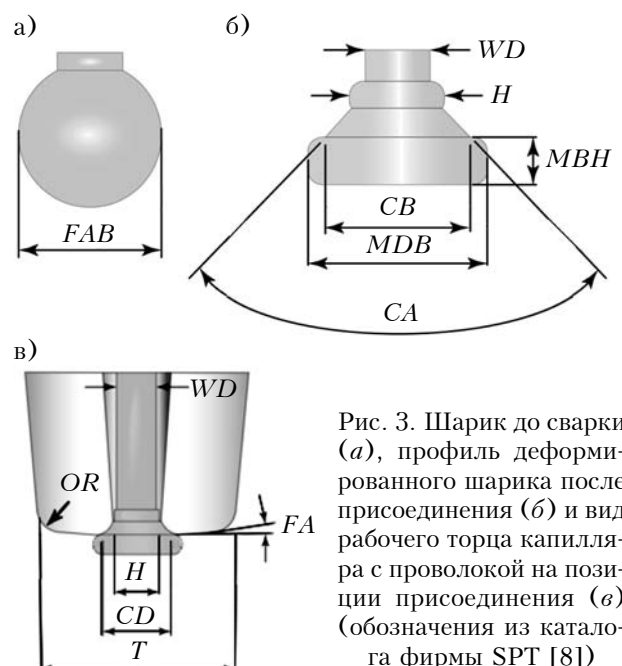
Шарик до сварки (а), профиль деформированного шарика после присоединения (б) и вид рабочего торца капилляра с проволокой на позиции присоединения (в) (обозначения из каталога фирмы SPT [8])
